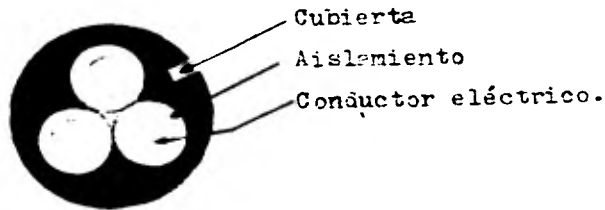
VISTA FRONTAL DEL RECUBRIMIENTO EXTRUIDO.
